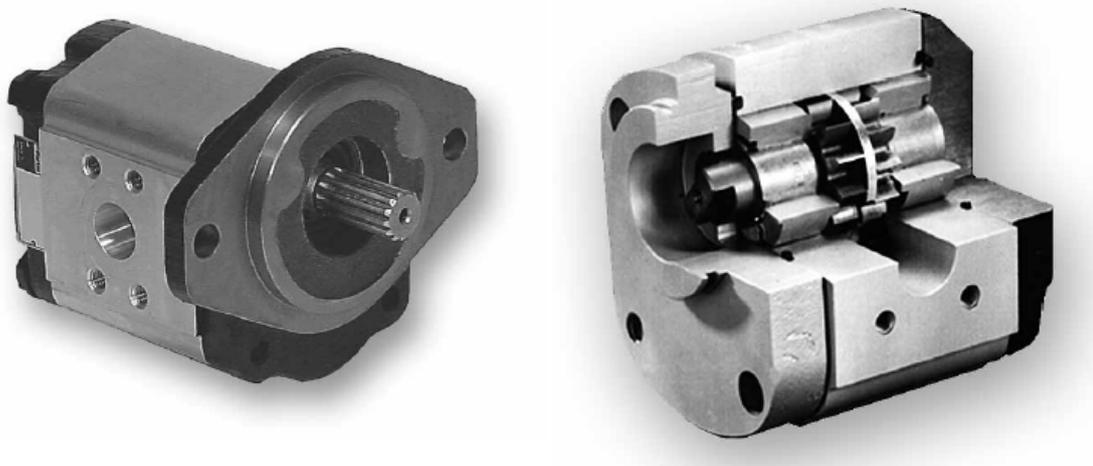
Шестеренный насос в алюминиевом корпусе серии PGP500 /35/
